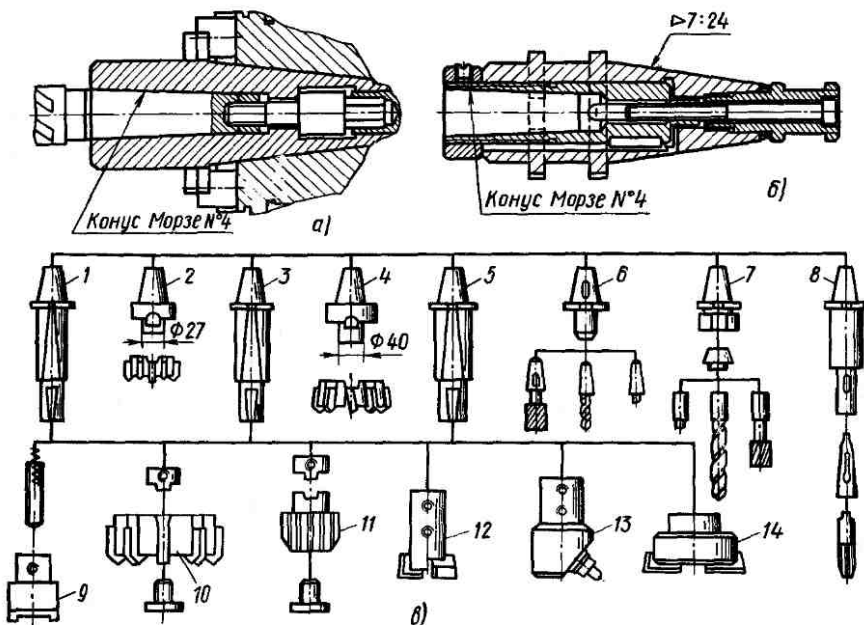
Вспомогательная оснастка для крепления осевого инструмента с резьбовым отверстием
